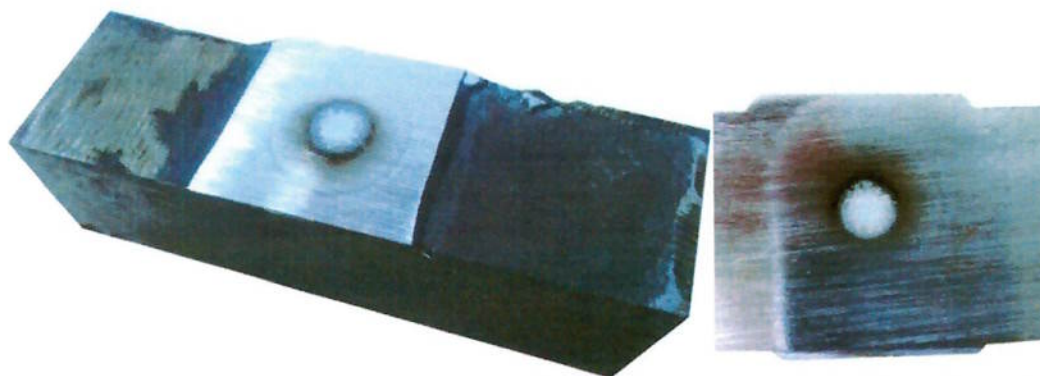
Análise Química do metal de solda realizada na face do cordão de solda e na intersecção dos cordões.
